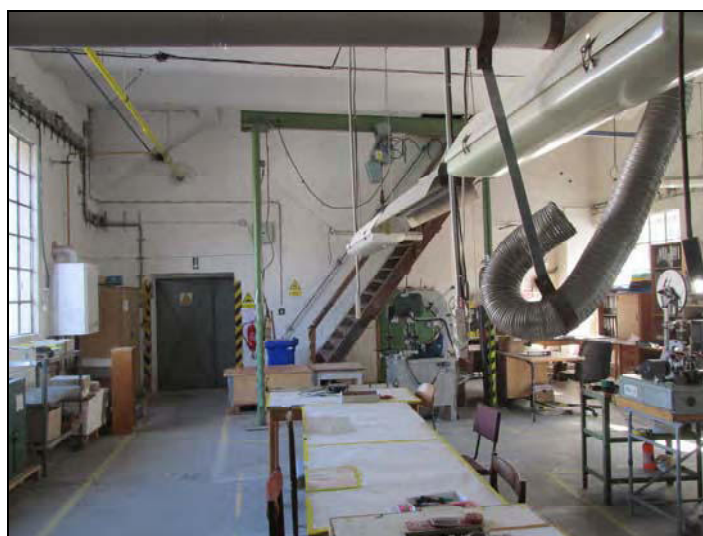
Interiér výrobních ploch – příprava materiálu
